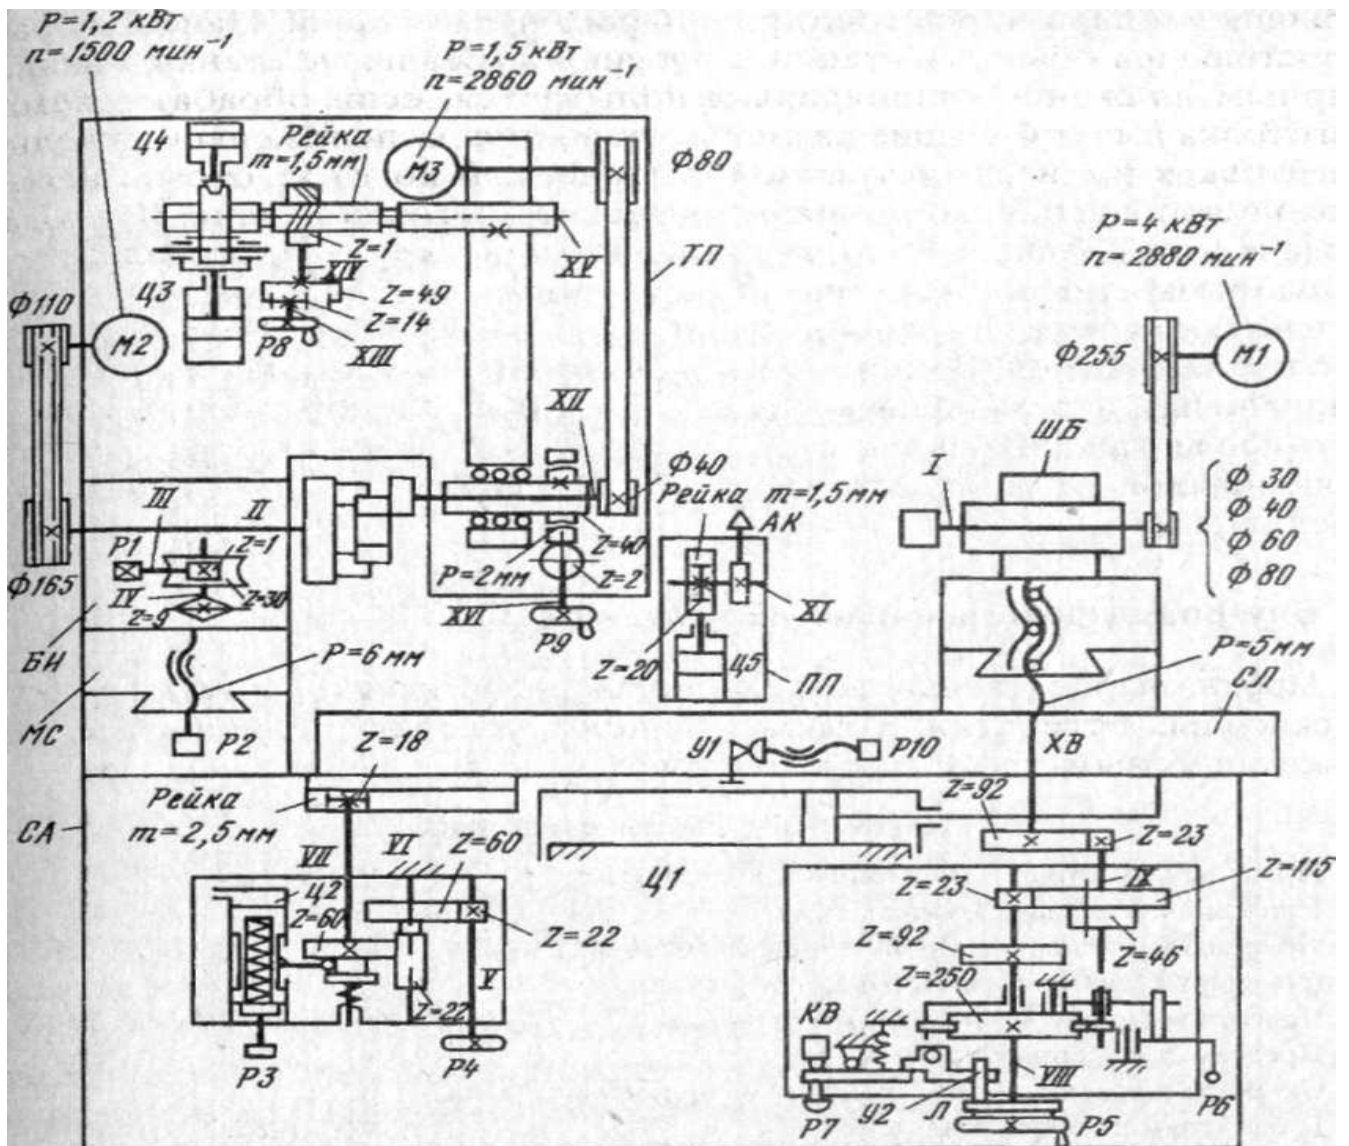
Кинематическая схема внутришлифовального станка мод. 3К227В: М1 - электродвигатель привода главного движения, М2 - электродвигатель круговой подачи, М3 - электродвигатель привода торцешлифовального приспособления, ШБ - шлифовальная бабка, ТП - торцешлифовальное приспособление, СЛ - стол, СА - станина, МС - мост, БИ - бабка изделия
